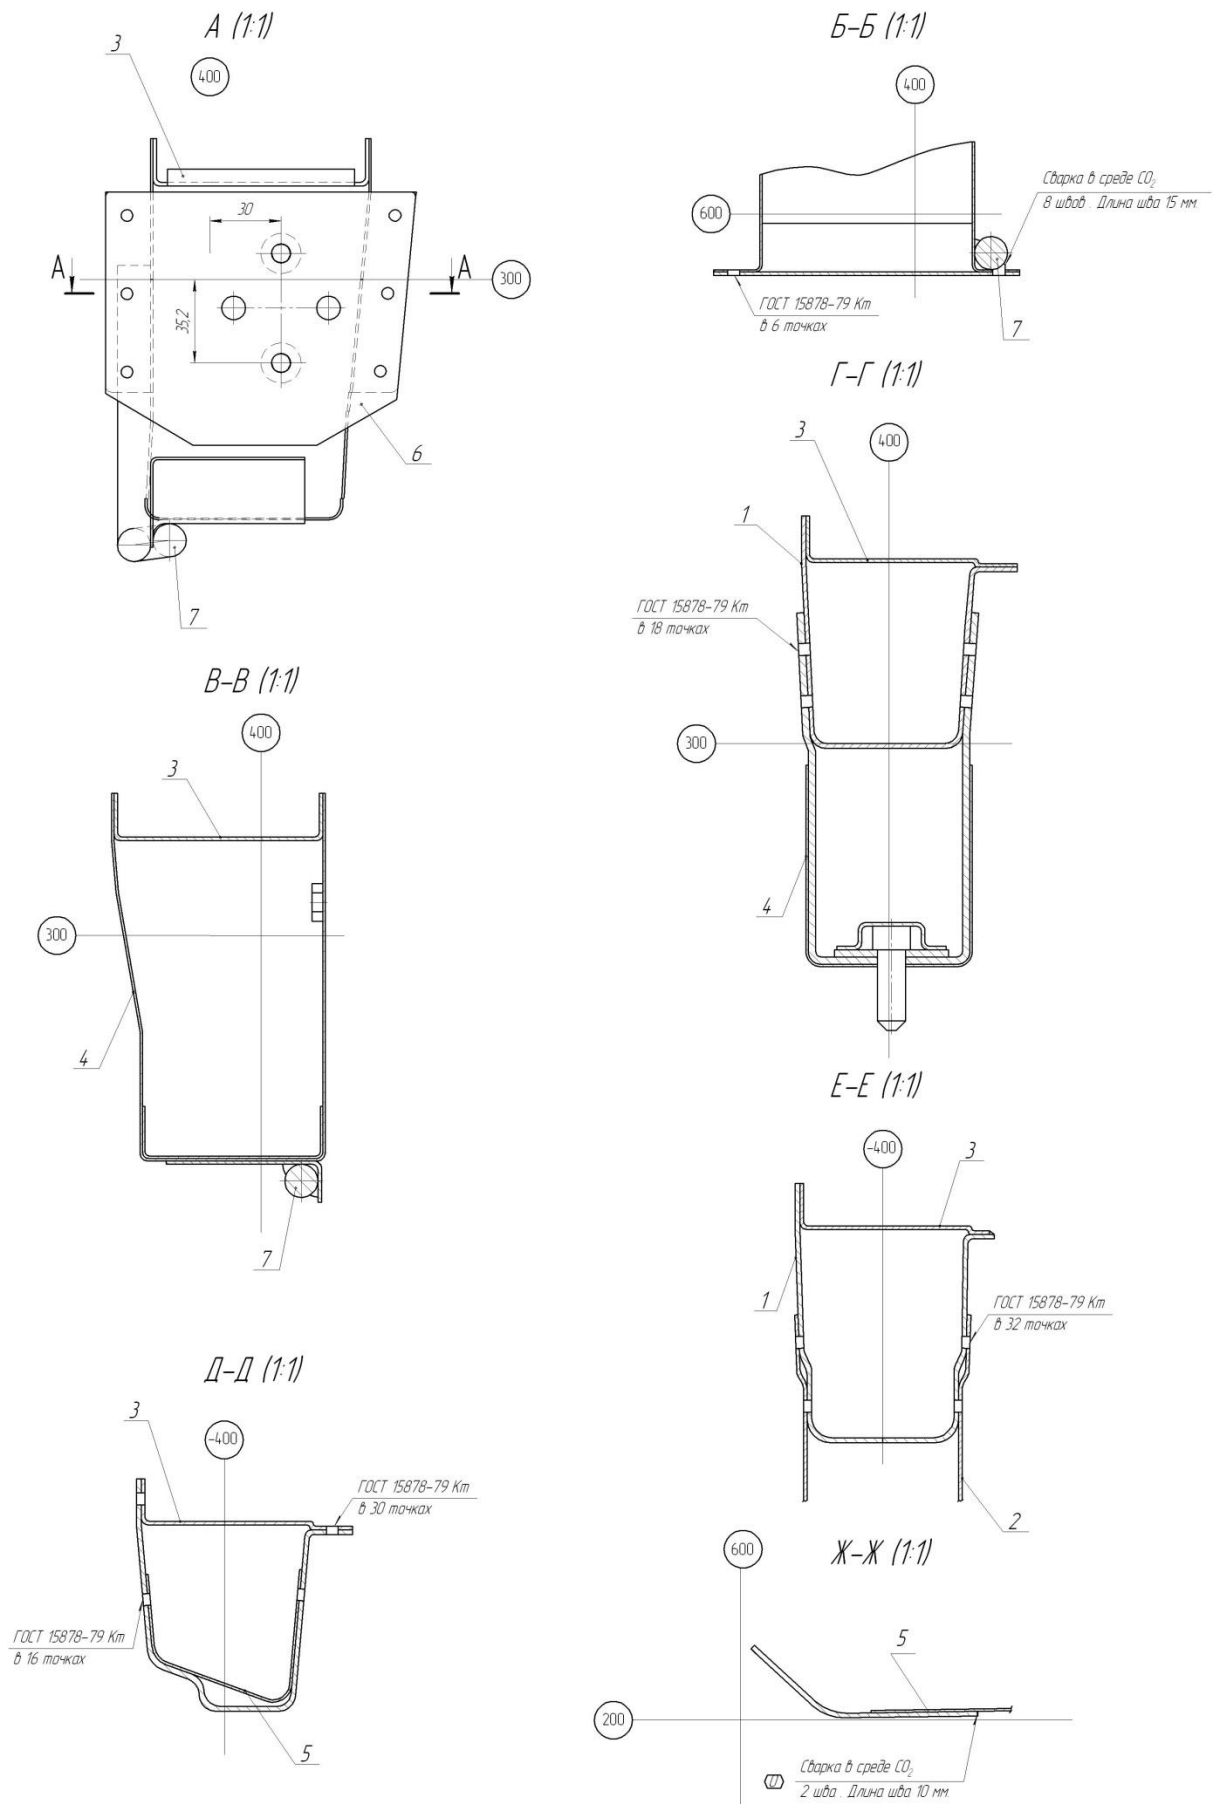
Сечения сварного узла и места выполнения сварных соединений
